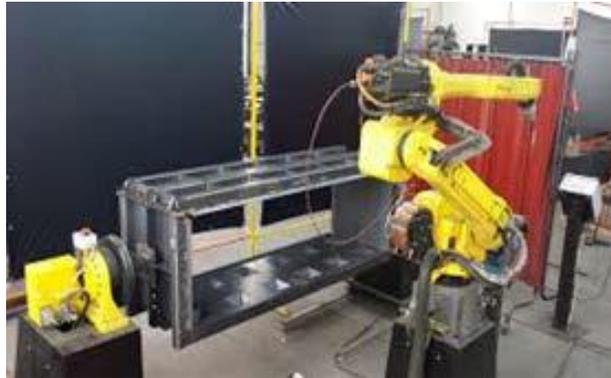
Sistema automatizado en la soldadura de moldajes.
